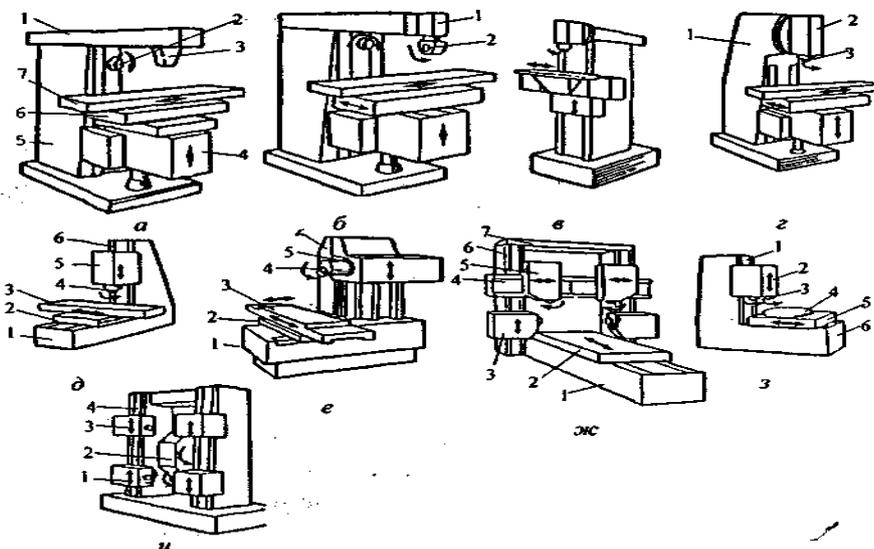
Схемы универсальных фрезерных станков и их основные формообразующие движения: *а* ~ универсальный консольный горизонтально-фрезерный; *б* - широкоуниверсальный консольный горизонтально-фрезерный; *в* - широкоуниверсальный бесконсольно-фрезерный; *г* - консольный вертикально-фрезерный; *д* - бесконсольный вертикально-фрезерный; *е* - бесконсольный горизонтально-фрезерный; *ж* - продольно-фрезерный; *з* - карусельно-фрезерный; *и* - барабанно-фрезерный.
